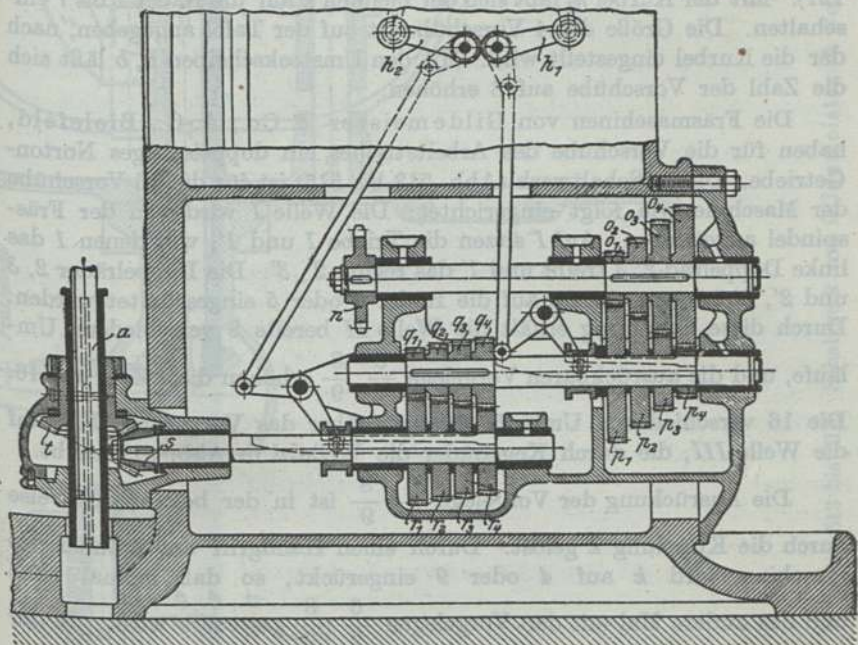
Ziehkeilschaltwerk der Wanderer-Fräsmaschine.
